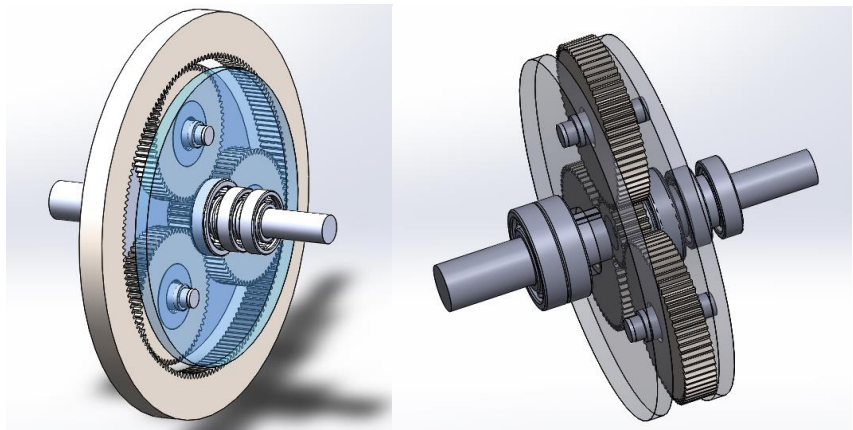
3D Poros & Planet Gear Single Stage Planetary
